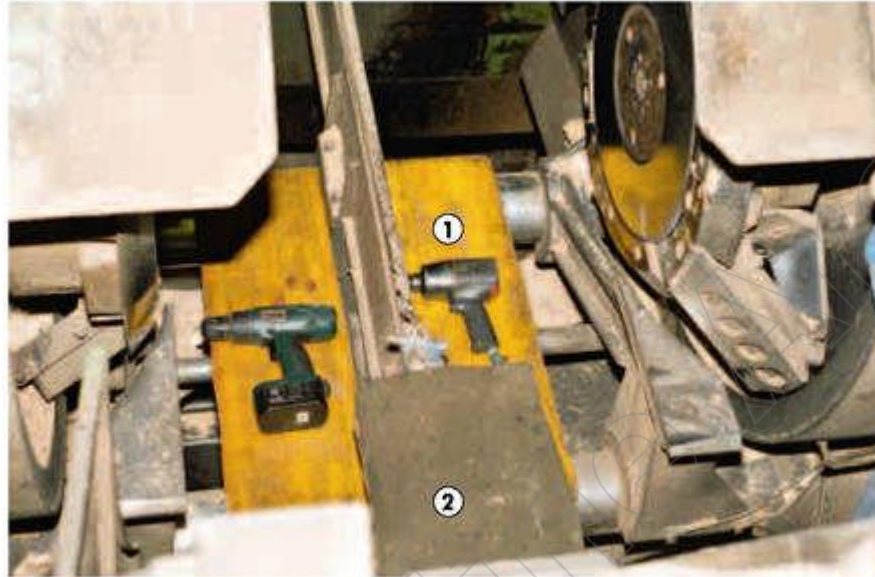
Standplatz zum Werkzeugwechsel an einem Spaner
